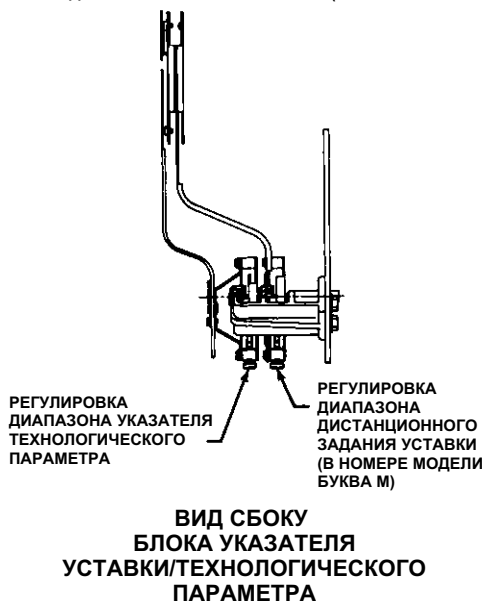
Расположение органов регулировки для калибровки контроллера Fisher 4196
